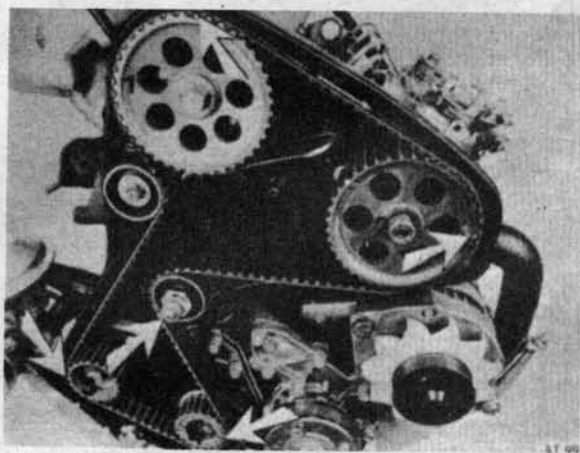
Положение меток на ремне привода механизма газораспределения и шкивах двигателя D16
